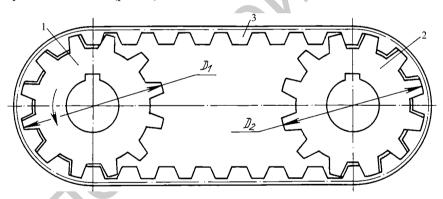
Схема зубчато-ременной передачи: 1, 2 – шкивы; 3 – ремень
